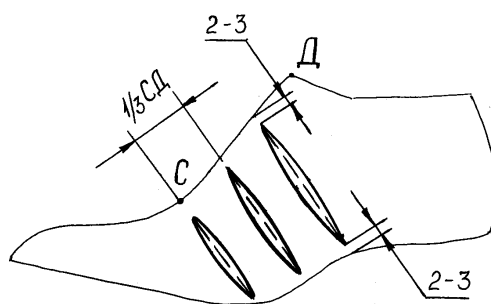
Розтин зліпка зовнішньої бічної поверхні колодки
